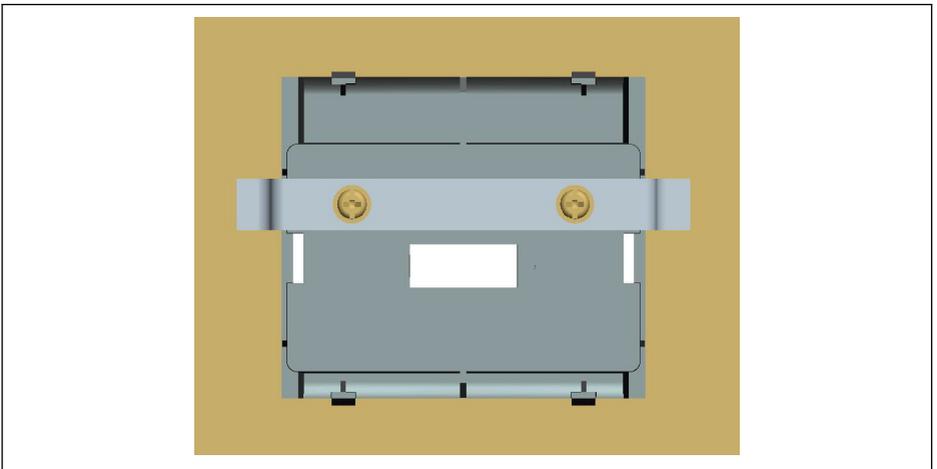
Fijar la placa de montaje (vista trasera)
